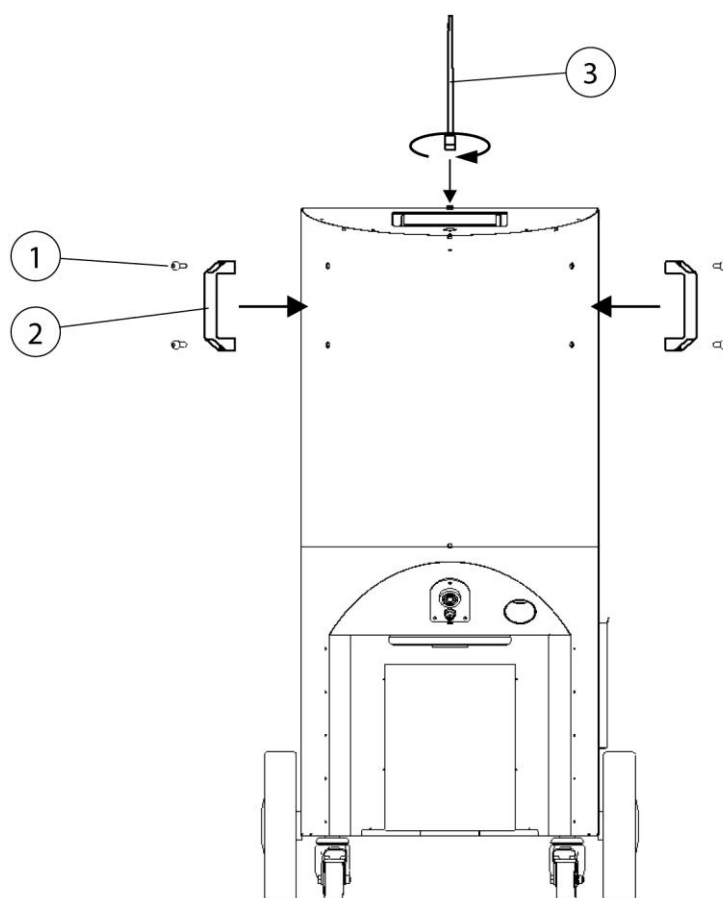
Montaje de las asas + Antena de telefonía móvil
